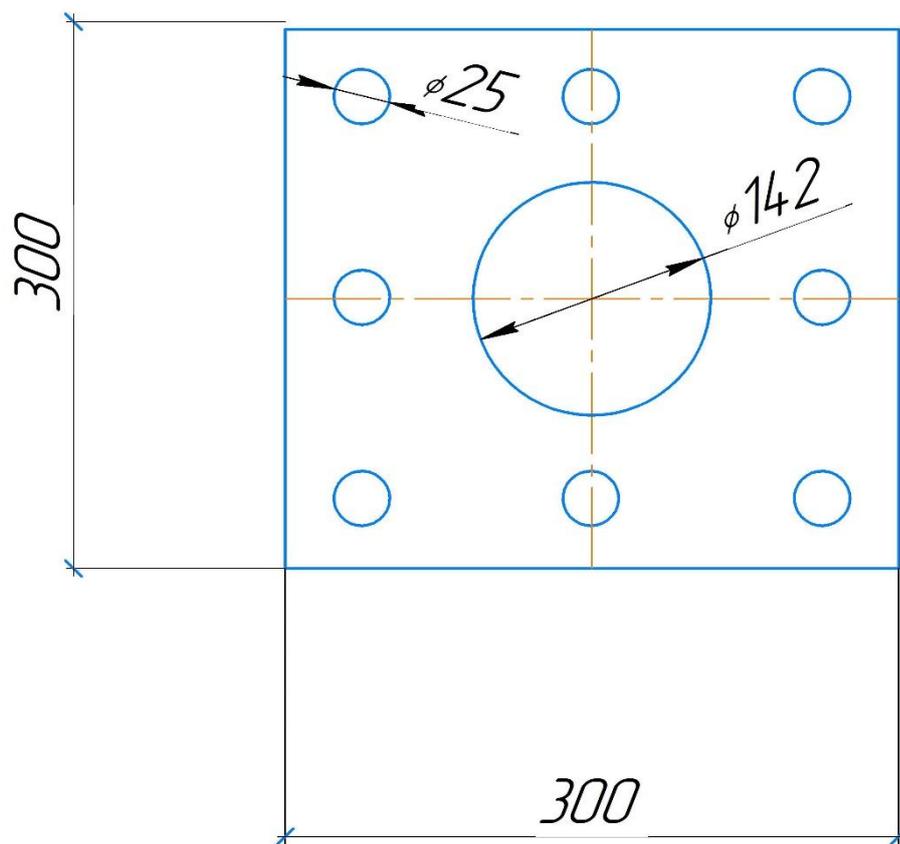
Плита с отверстием под трубу для сварки
